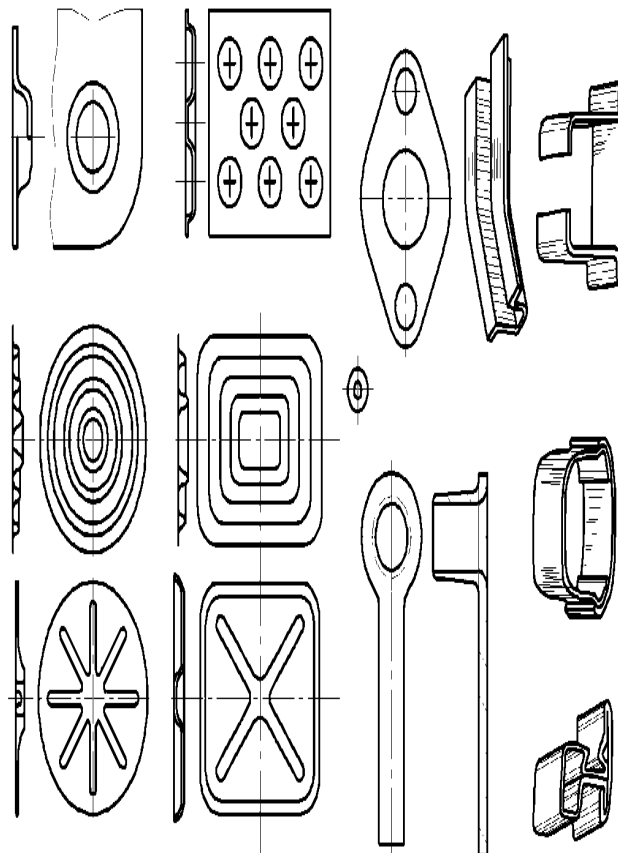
Деталі, що виготовляються холодним листовим штампуванням
